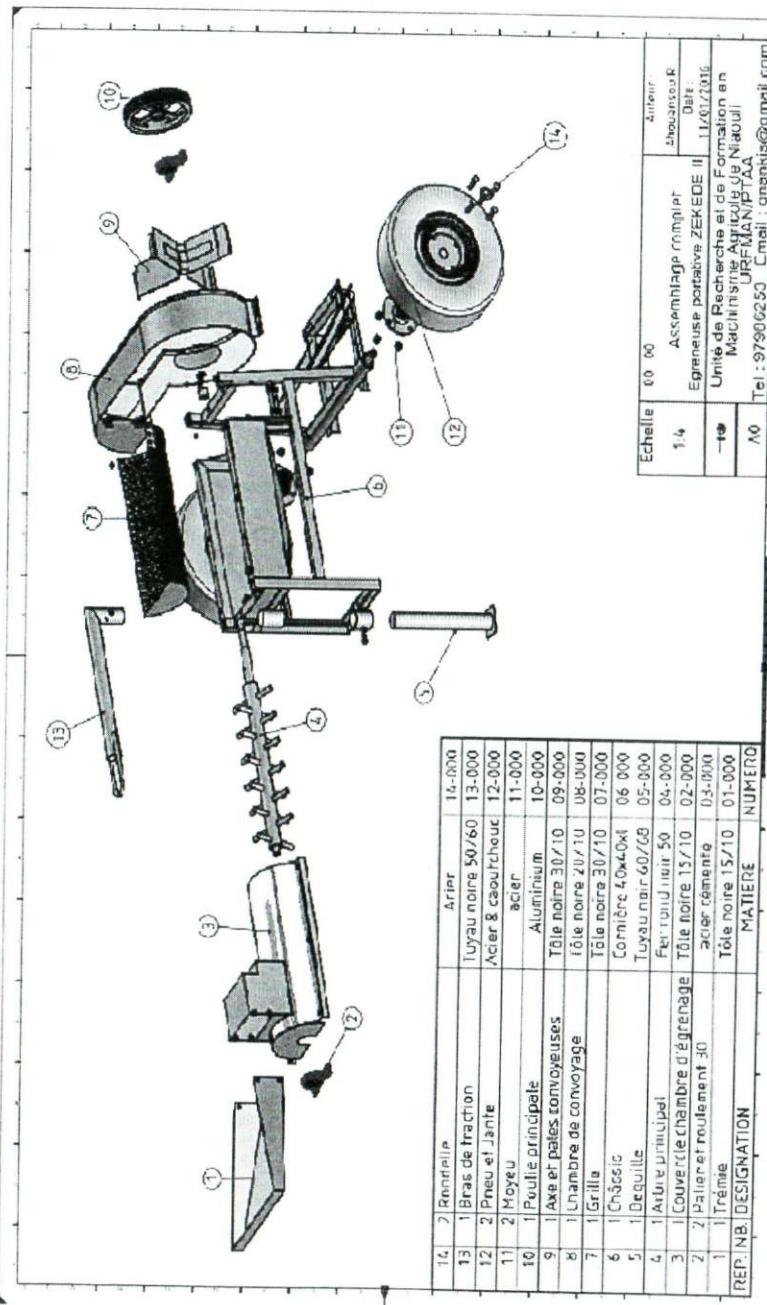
Vue éclatée assemblage égreneuse ZEKEDÉ II
